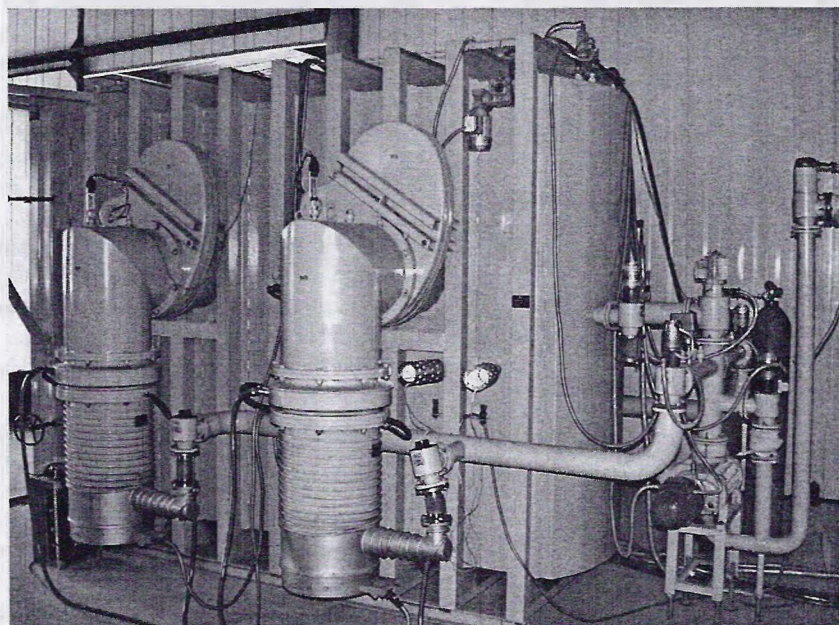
Установка VATT 1600x2400-ЭД. Вид сбоку
